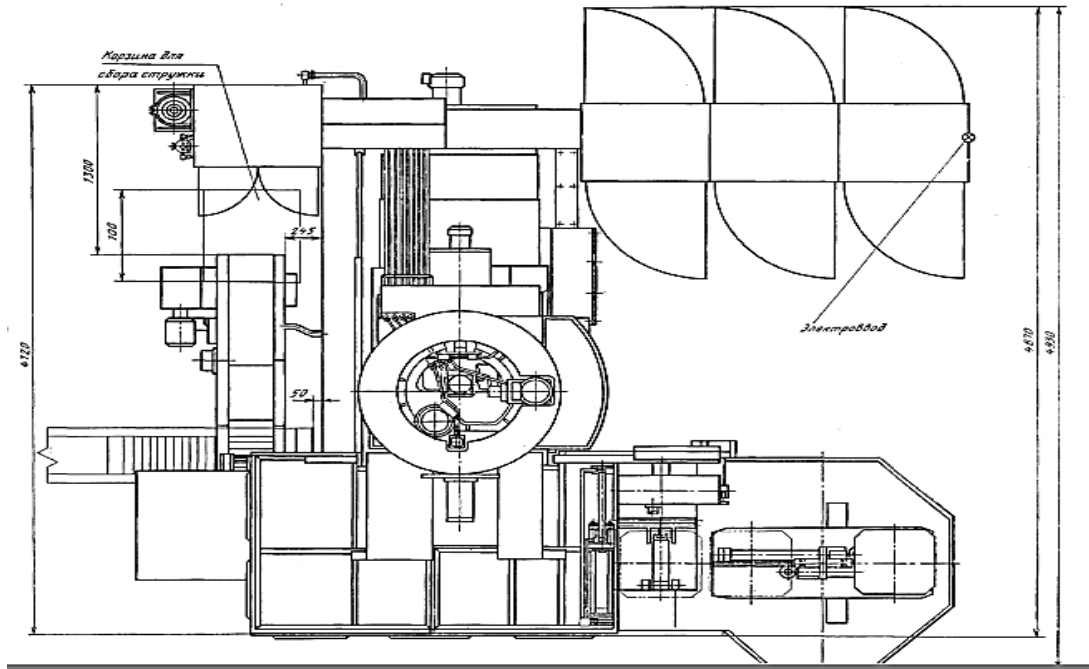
Загальний вид верстата (вид зверху) із двомісним накопичувачем
